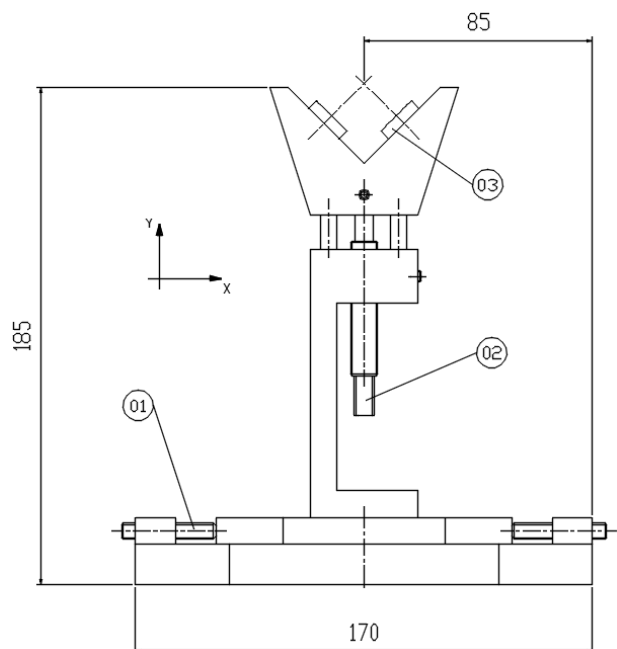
Desenho técnico do mancal protótipo (dimensões em milímetros).
